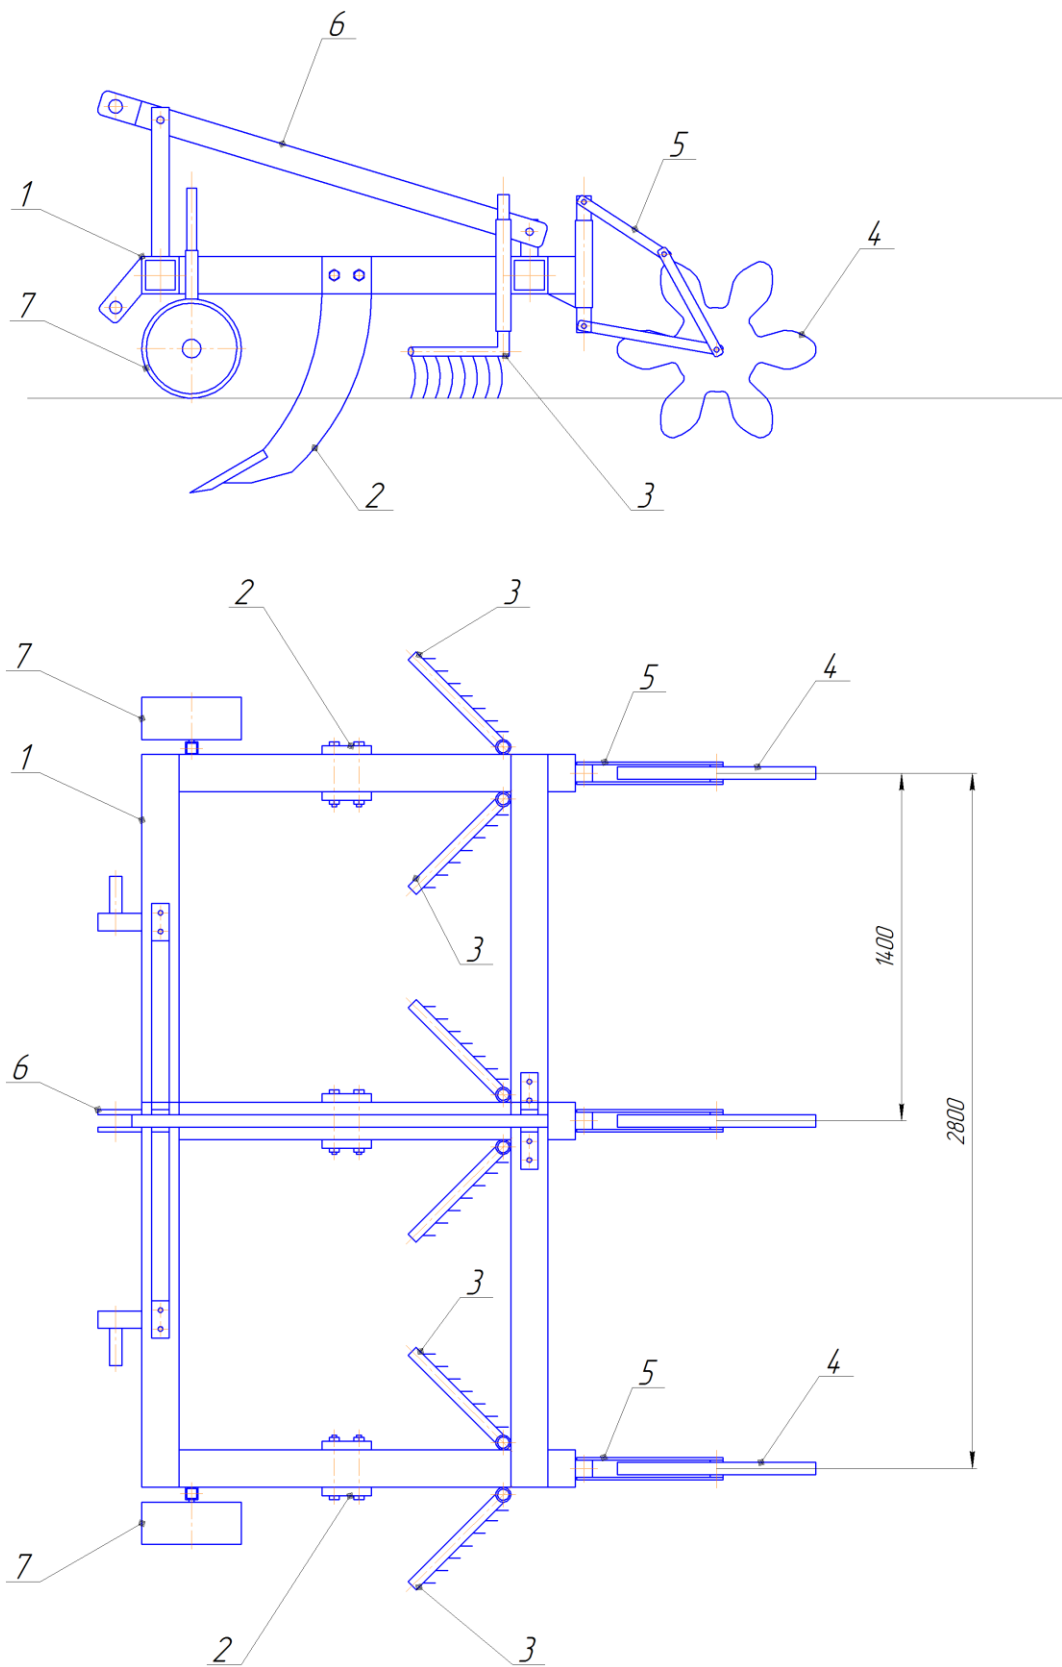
Общая схема щелевателя: 1 – рама; 2 – щелерез; 3 – граблина соломонаправителя; 4 – заделывающий диск; 5 – параллелограммный механизм; 6 – навеска; 7 – опорное колесо
